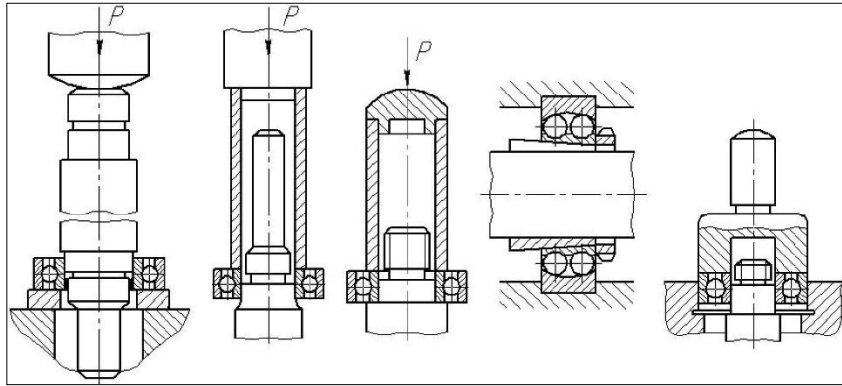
Встановлення підшипників на вал і в корпус деталі
